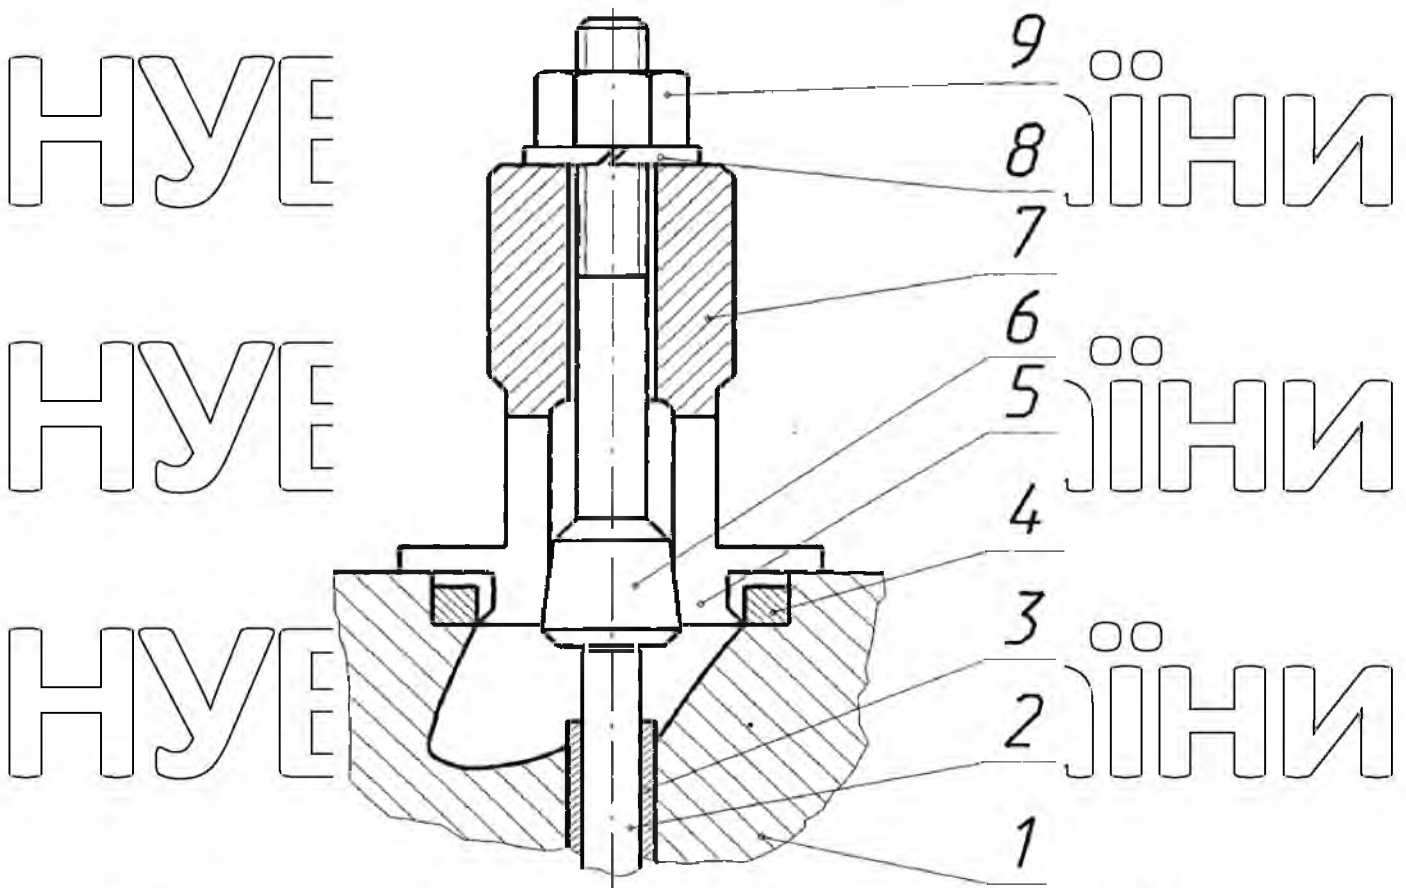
Пристрій для пресування сідла клапанів з ГБД: 1 - головка блоку; 2 - стрижень; 3 - напрямна втулка; 4 - сідло клапана; 5 - цангова ручка; 6 - конус; 7 - корпус екстрактора; 8 - шайба; 9 - гайка.
